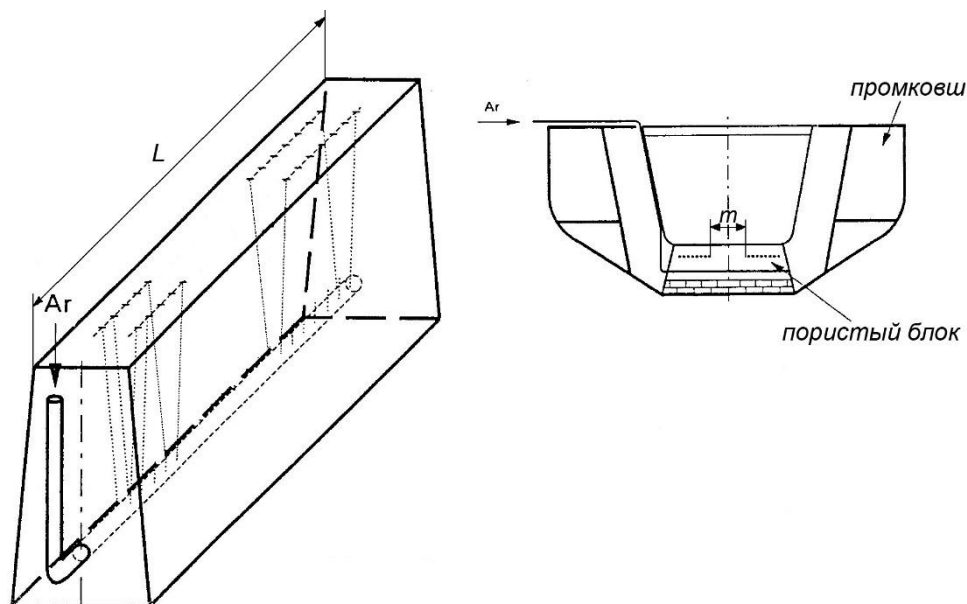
Конструкция продувочного блока промежуточного ковша
